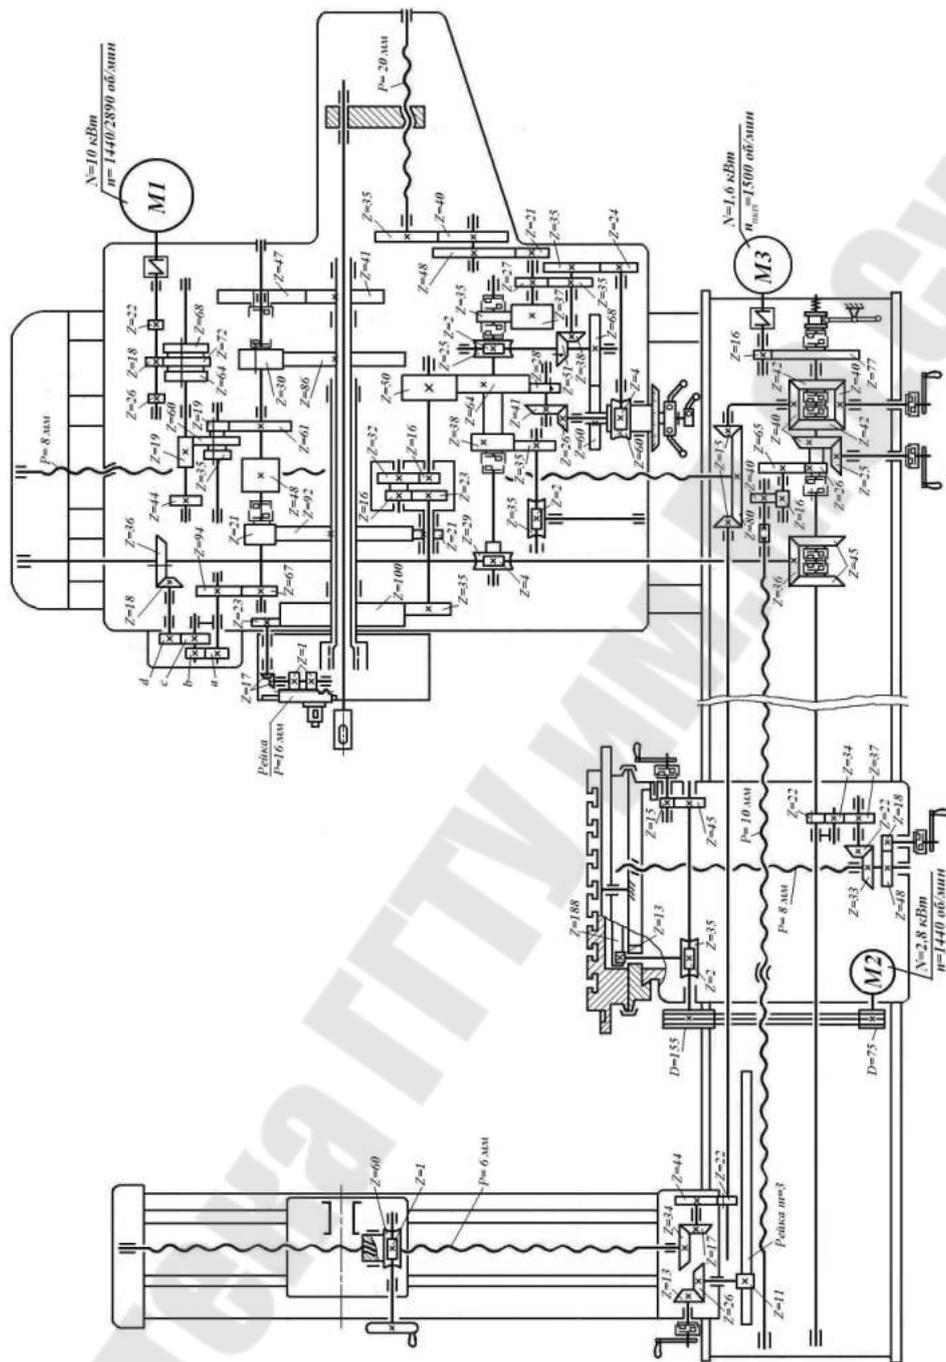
Кинематическая схема горизонтально-расточного станка 2620 А
